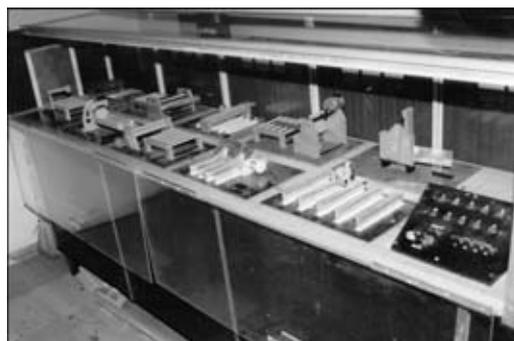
Макеты механического и сварочного оборудования для изготовления двутавровых балок (линия)
